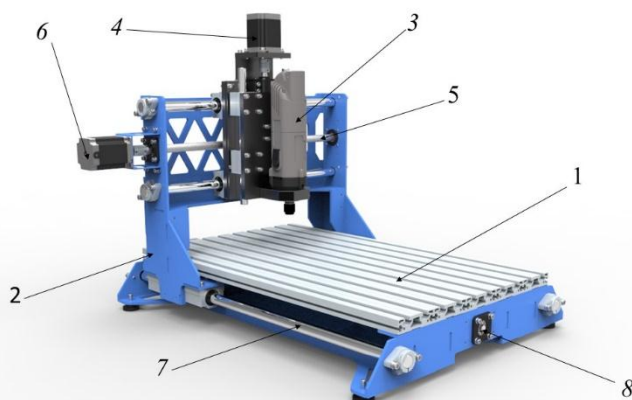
Общий вид 3D модели мини-фрезерного ЧПУ станка.
